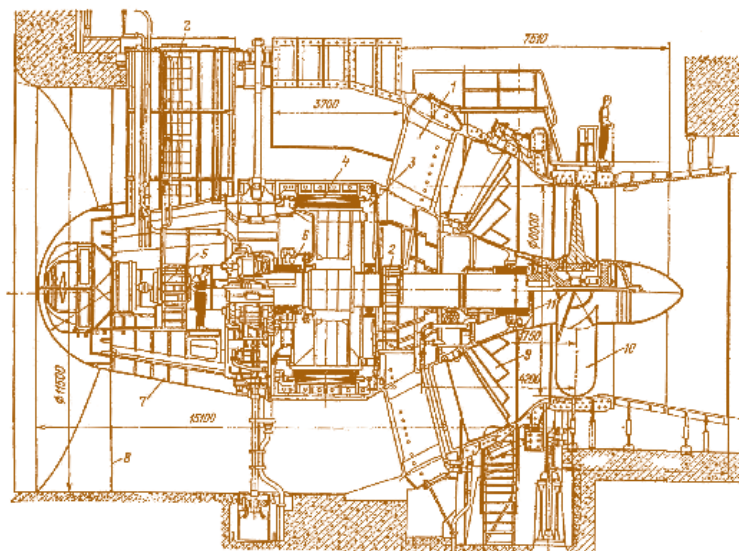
Капсульний агрегат Київської ГЕС: 1 – колони статора; 2 – шахта; 3 і 4 – ротор і статор генератора; 5 – масловодоприймач; 6 – під'ятник; 7 – капсула; 8 – бичок; 9 – напрямний апарат; 10 – робоче колесо турбіни; 11 – турбінний підшипник
